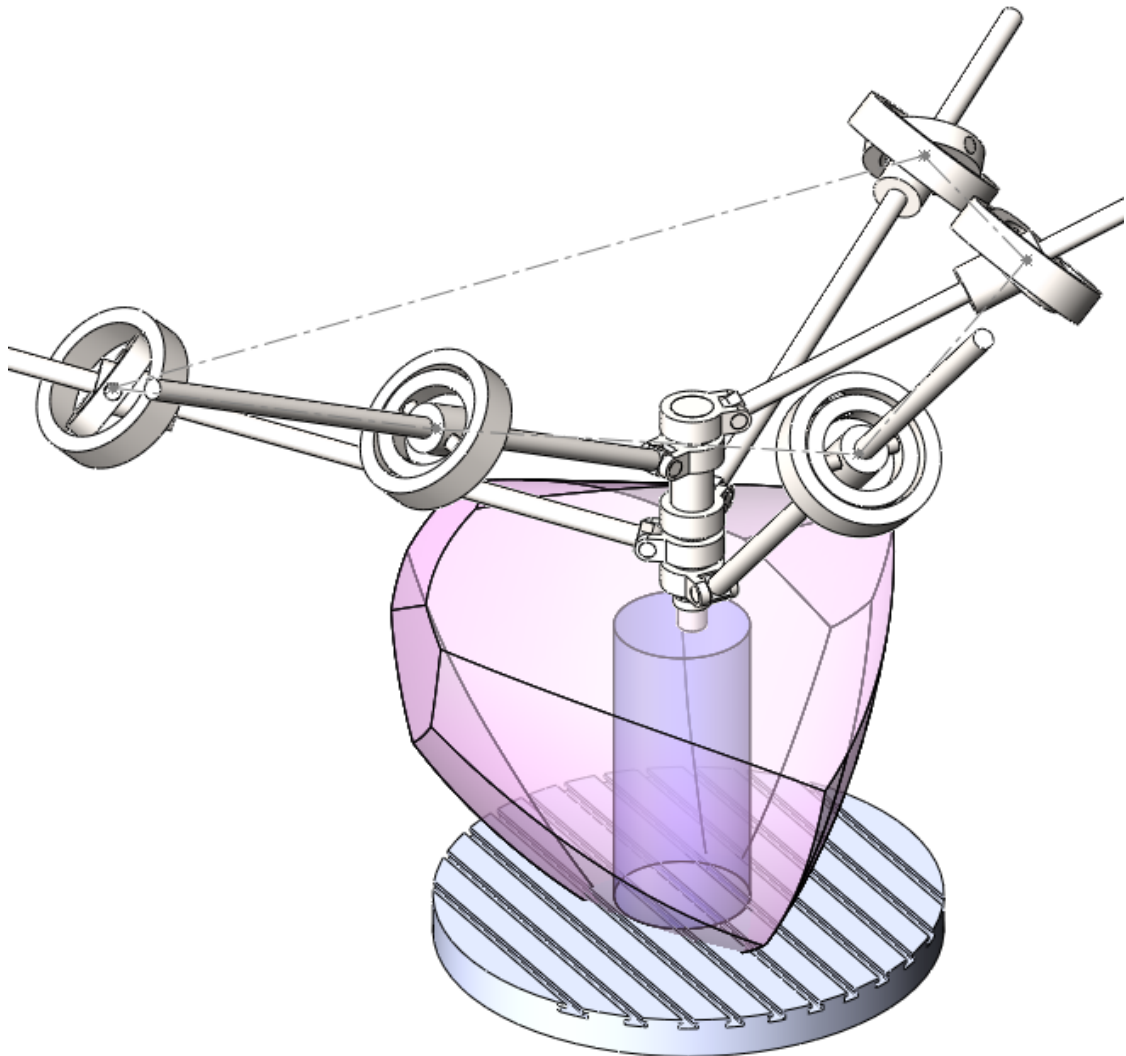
Максимальні габарити заготовки при нижньому положенні столу
